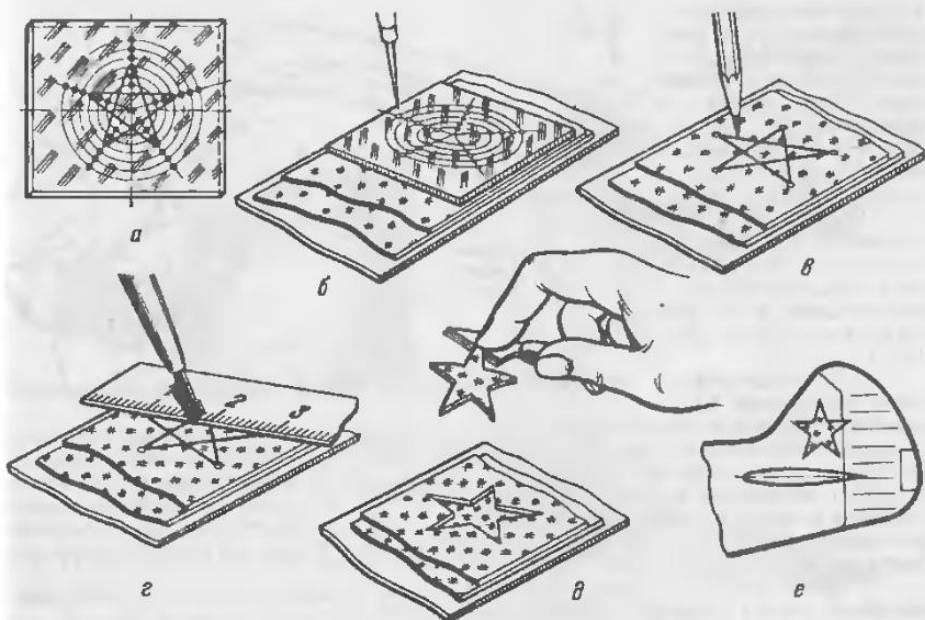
Последовательность операций при изготовлении шаблона и маски опознавательного знака (звезды): а - изготовление трафарета-шаблона; б - разметка на липкой ленте; в - прочерчивание; г - прорезка; д - выемка готовой маски; е - маска нанесена на поверхность модели
